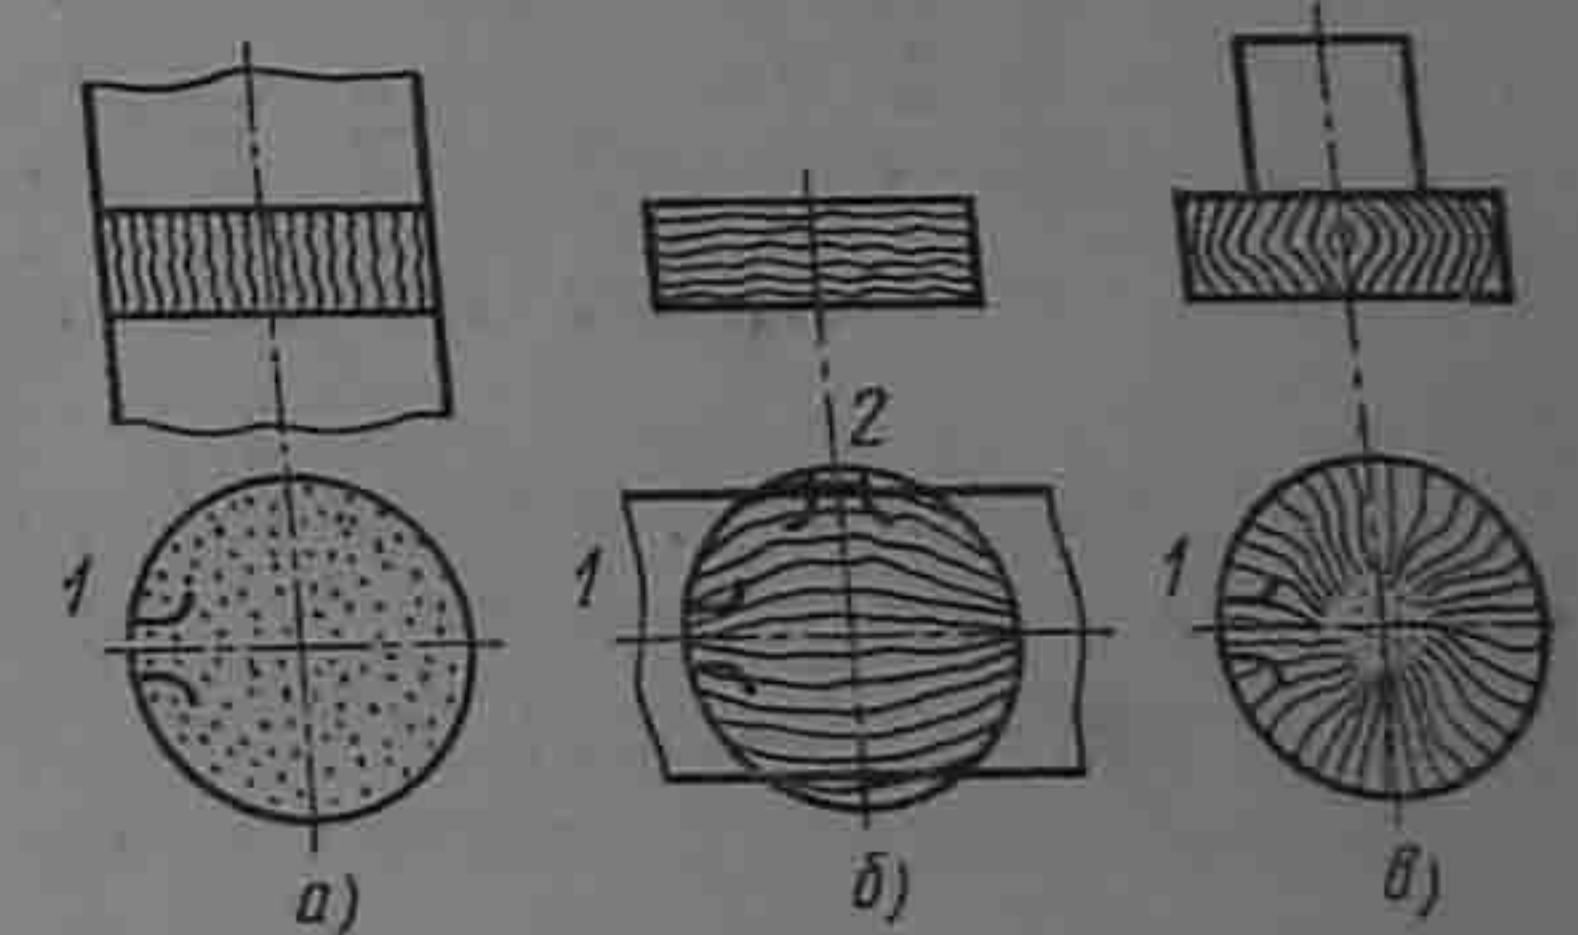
Схема макроструктуры зубчатых колес, изготовленных различными способами
